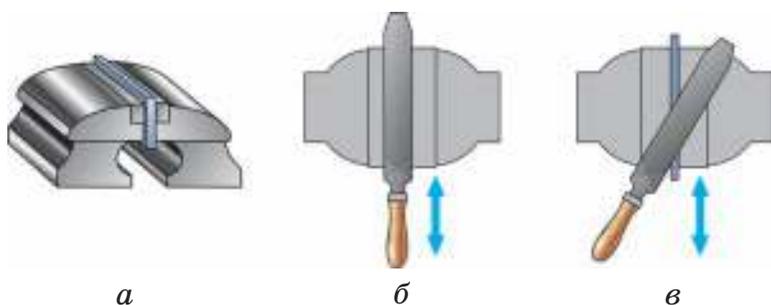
Зачистка кромок заготовок из тонколистового металла в тисках:
